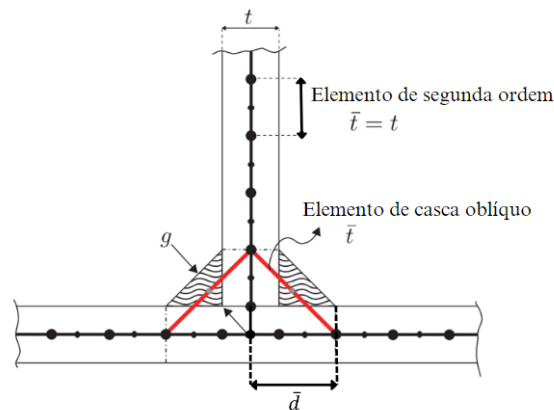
Cordão de solda modelado via elementos em casca oblíquo [Adaptada de Echer e Marczak, 2018].
